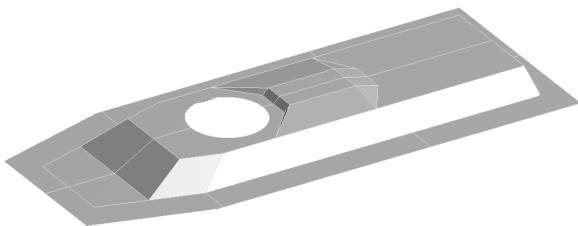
Поверхнева геометрична модель макету у пакеті SolidWorks
